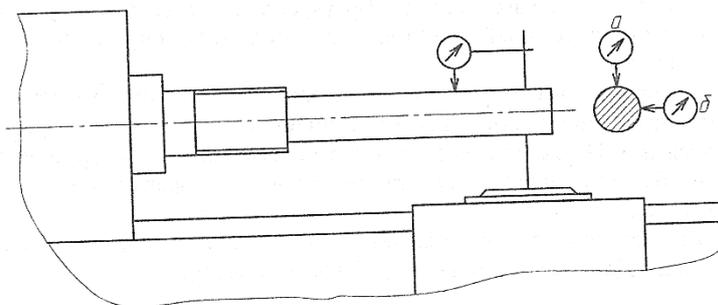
Схема установки индикатора для проверки радиального биения, центрирующей шейки шпинделя
